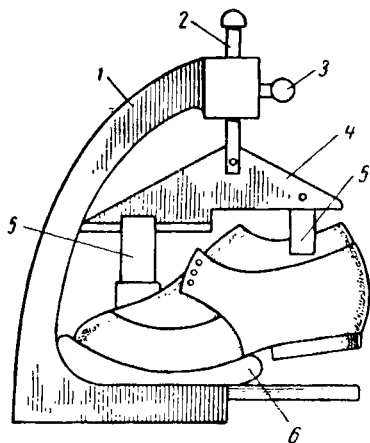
Запрессовка обуви в секции пневматического пресса ППП-Р: 1—стойка, 2—рейка, 3—фиксатор, 4—коромысло, 5—упоры, 6—покрывка
